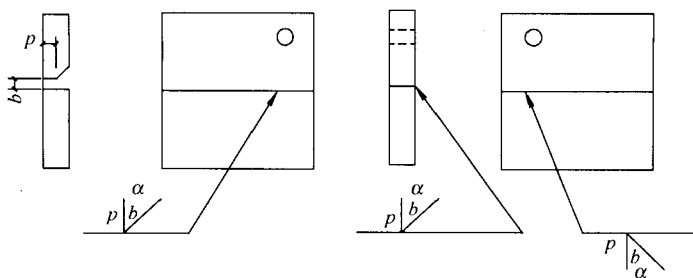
一个焊件带坡口的焊缝标注方法
